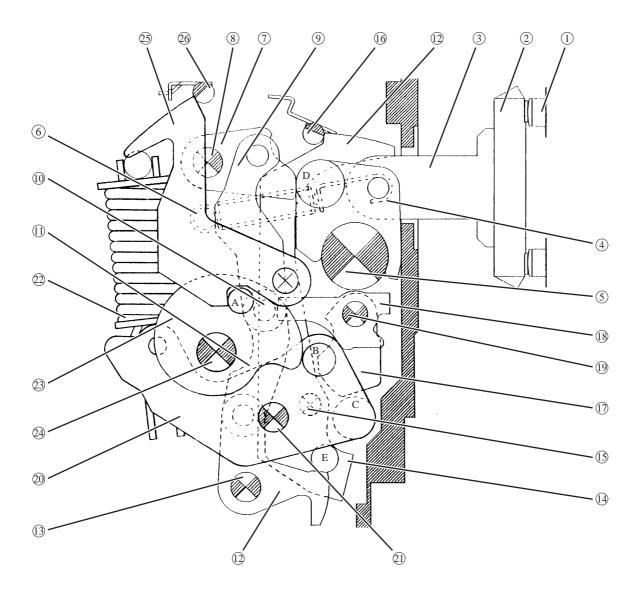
Meccanismo (interruttore chiuso "ON" e molle di chiusura cariche "CHARGED")
